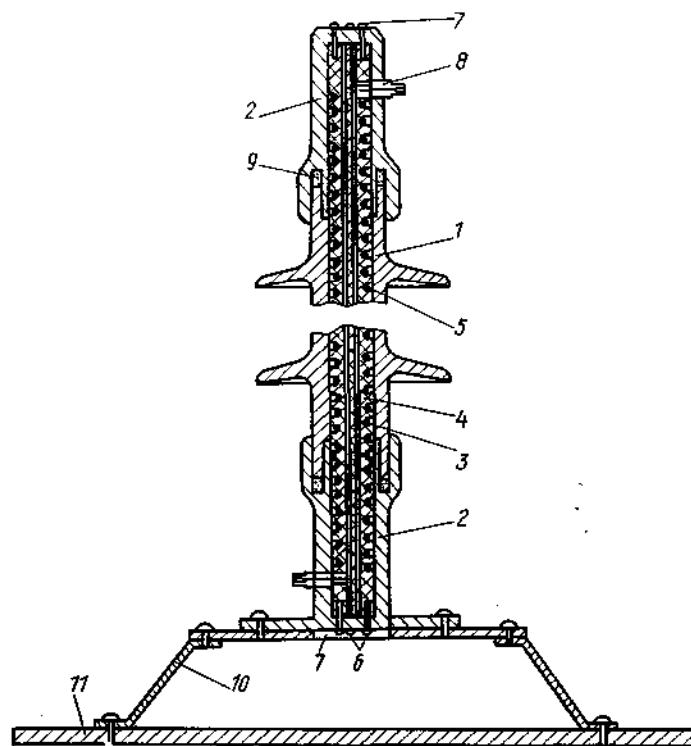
Жесткая опорная изоляционная конструкция со световодом, рассчитанная на умеренные напряжения:
